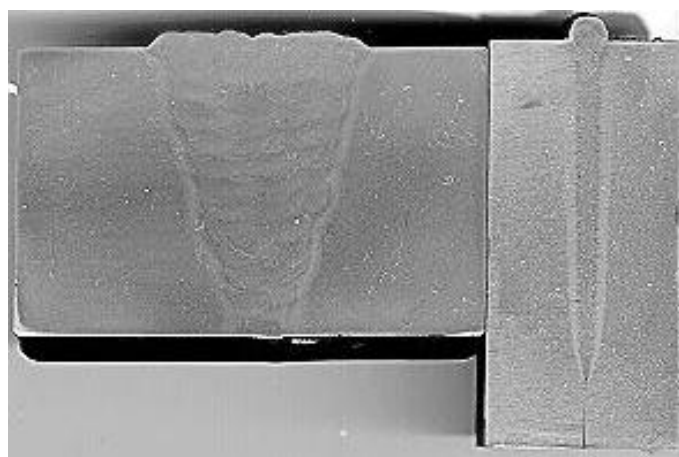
Comparaison d'une soudure à multi passage conventionnelle de TIG (gauche) avec une soudure du passage simple EB de profondeur semblable
